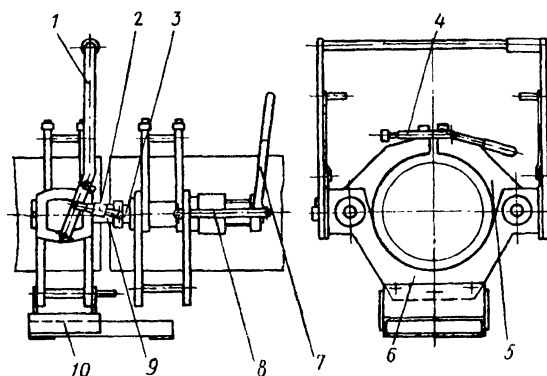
Сварочное монтажное устройство УСПМ-225 с рычажным приводом:
